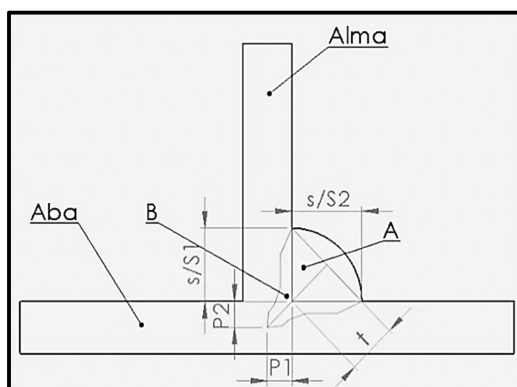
Principais características geométricas da junta soldada de filete.
